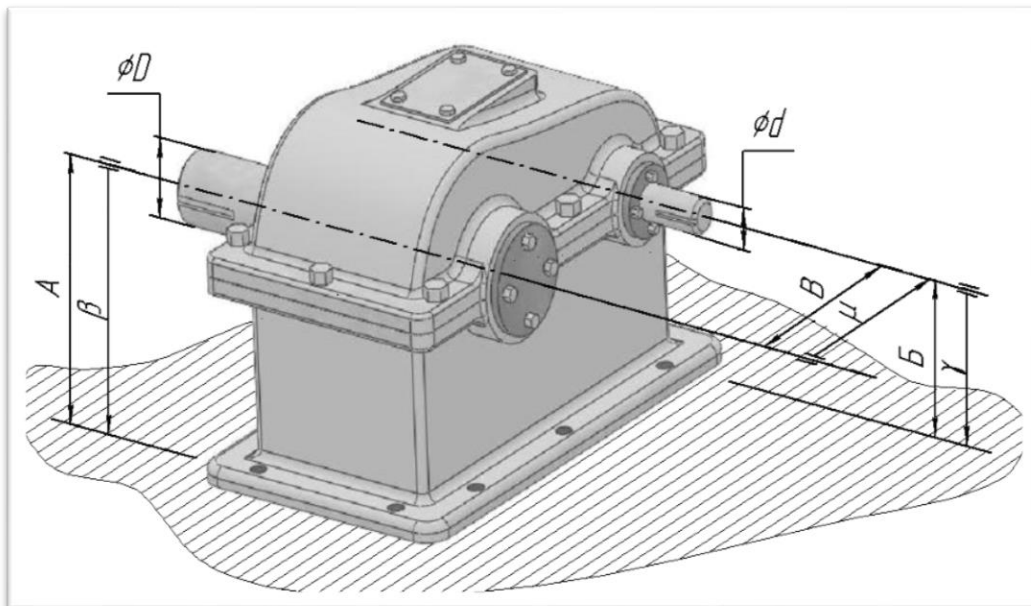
Розмірні зв'язки виконавчих поверхонь редуктора
